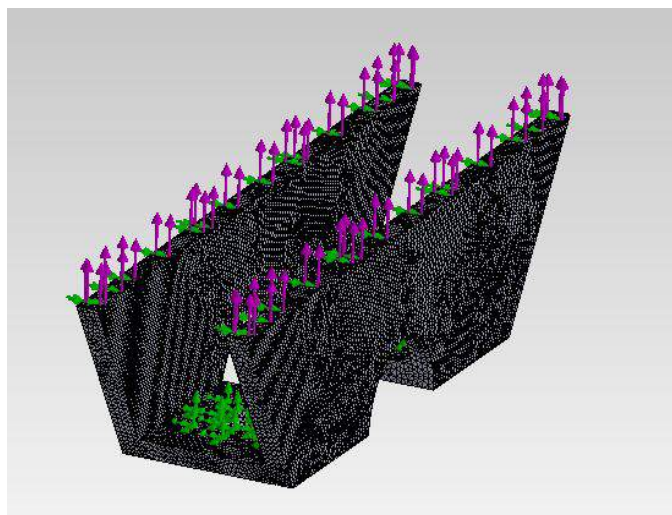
Malla pieza sujeción eje horizontal con cargas hacia abajo.
